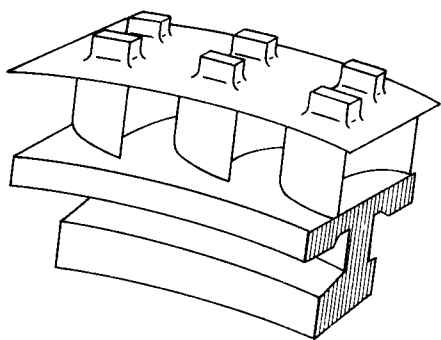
Сварной пакет из трех лопаток регулирующей ступени турбины К-800-240 ЛМЗ
